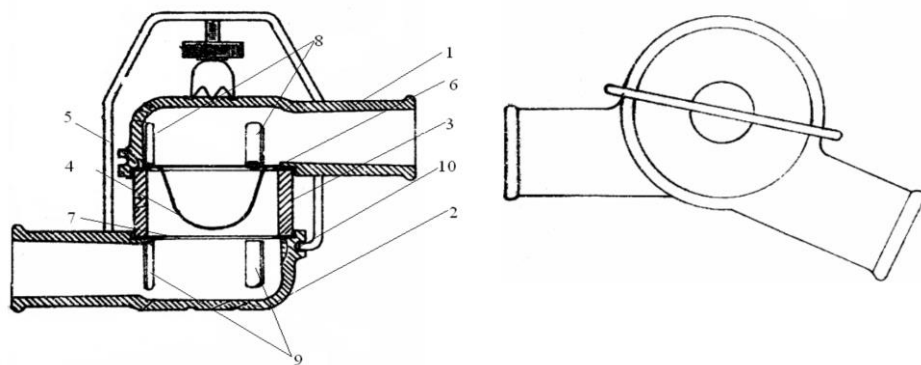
Схема фільтра для очищення потоку рідини (патент Австралії № 67952/81): 1 – вхідний патрубок; 2 – вихідний патрубок; 3 – прозорий вертикальний корпус; 4 – чашоподібний сітчастий фільтр; 5 – сполучна П – образна дрютяна рамка; 6 – відбортована кромка чашоподібного сітчастого фільтра; 7 – прокладка; 8,9 – патрубки, що забезпечують обертальний рух рідини при проходженні через фільтр; 10 – гвинтовий притиск
